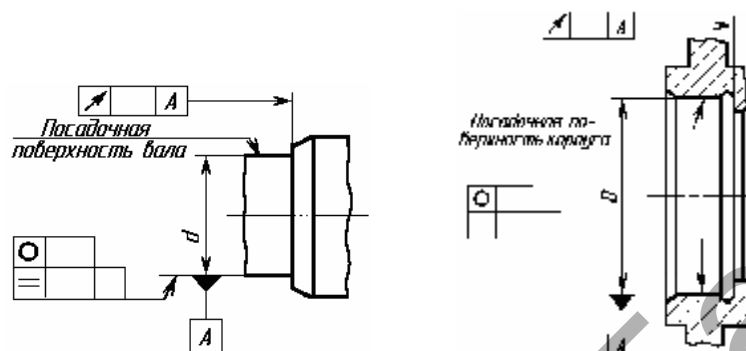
Назначение полей допусков формы и расположения поверхностей вала и корпуса, сопрягаемых с подшипником
